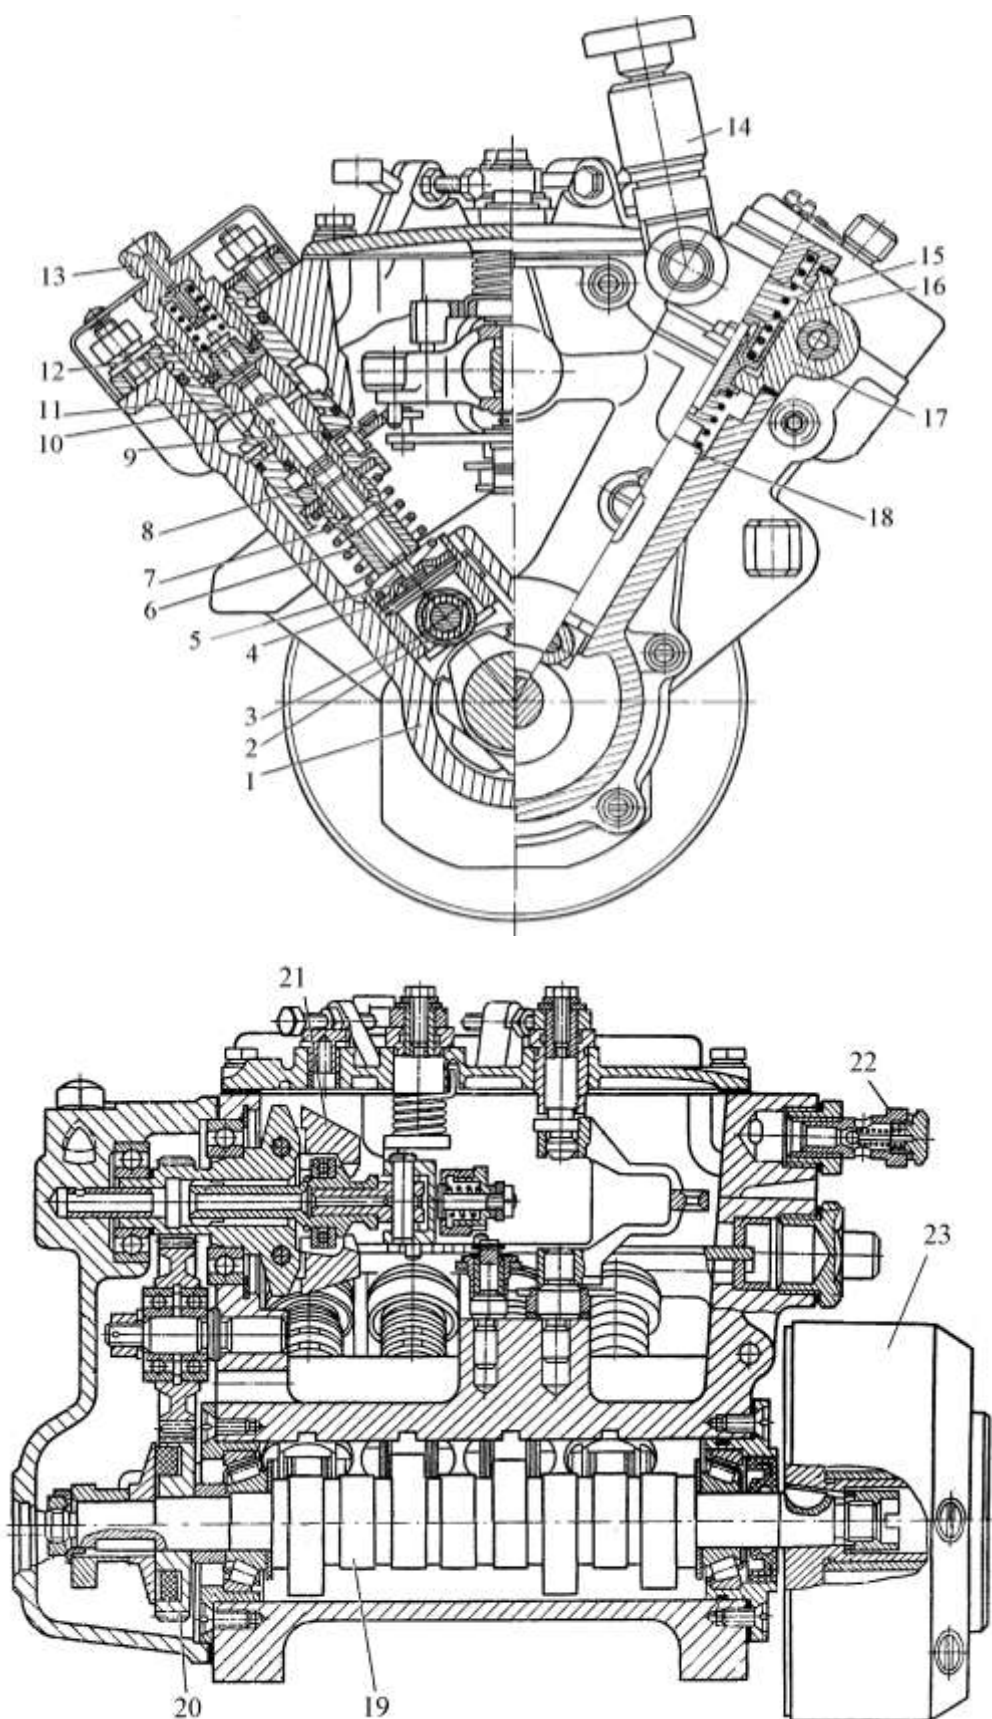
V-образный ТНВД дизеля КамАЗ модели 33-02: 1 - корпус; 2 - ролик; 3 - ось; 4 - толкатель; 5 - тарелка пружины; 6 - поворотная втулка; 7 - пружина; 8 - плунжер; 9 - правая рейка; 10 - втулка плунжера; 11 - корпус секции; 12 - нагнетательный клапан; 13 - штуцер; 14 - ТПН; 15 - пружина; 16 - поршень ТПН; 17 - корпус насоса; 18 - толкатель ТПН; 19 - кулачковый вал; 20 - ведущая шестерня регулятора; 21 - груз; 22 - перепускной клапан; 23 - муфта УОВТ.
